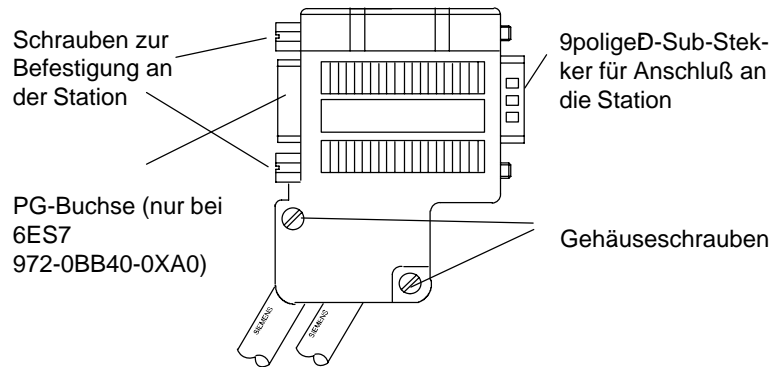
Busanschlußstecker (Bestellnummer 6ES7 972-0B.40 ...)
